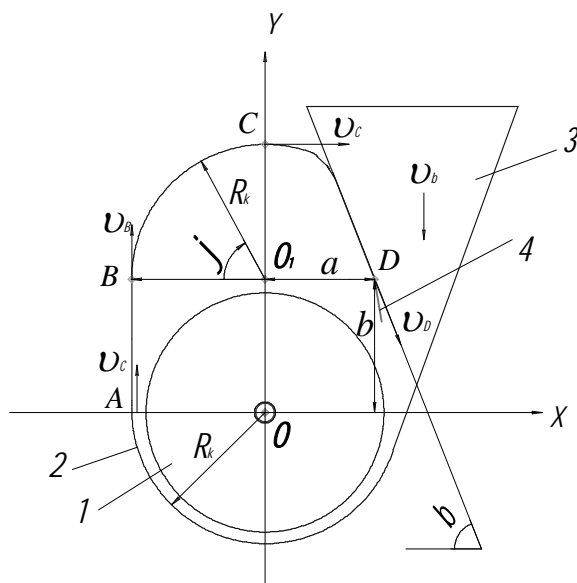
Схема визначення форми робочої поверхні кожуха дозатора - змішувача в зоні завантаження:
